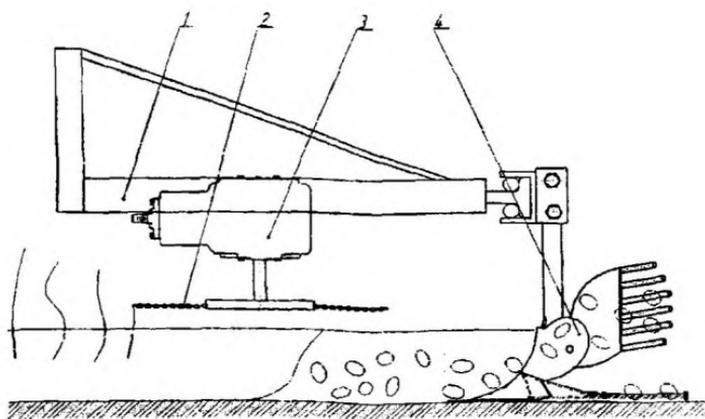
Общий вид измельчающе-подкапывающего агрегата
